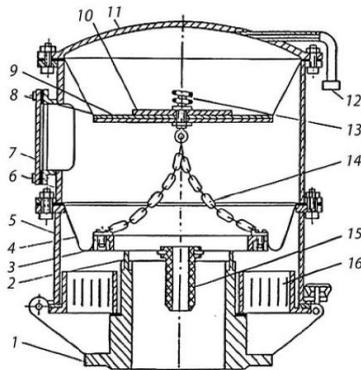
Дыхательный клапан НДКМ: 1 – соединительный патрубкок; 2 – седло; 3 – тарелка; 4 – мембрана; 5 – нижняя часть корпуса; 6 – верхняя часть корпуса; 7 – боковой люк; 8 – верхняя мембрана; 9 – диски; 10 – регулировочные грузы; 11 – крышка; 12 – трубка; 13 – амортизаторная пружина; 14 – цепочки для соединения дисков; 15 – импульсная трубка; 16 – огневой предохранитель
